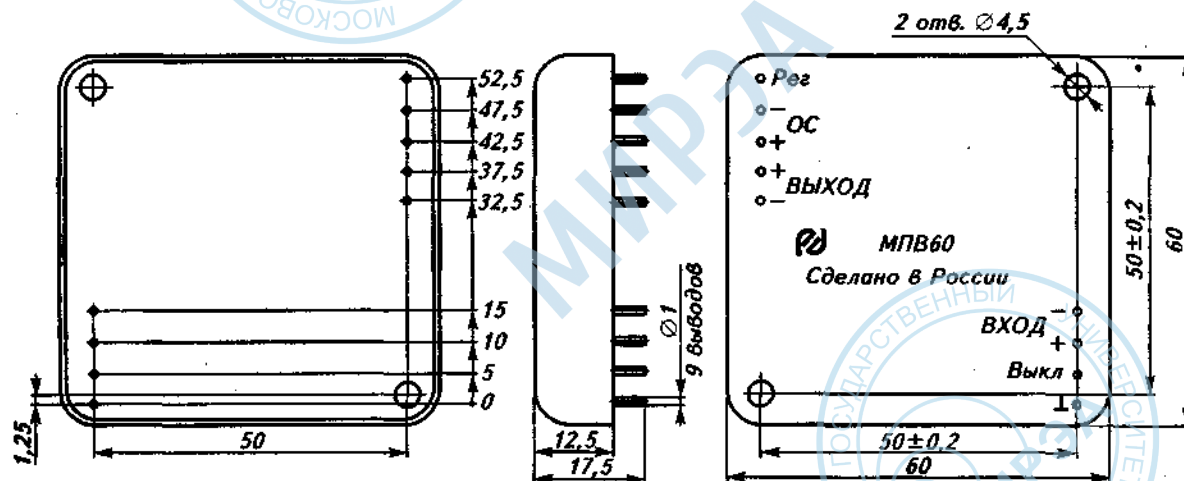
Общий вид, габаритные и присоединительные размеры модулей питания МПВ60 и МПЕ60
